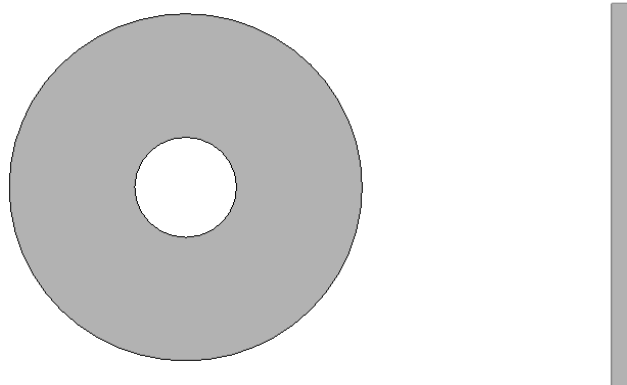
Vista en planta y perfil del pie de la válvula de impulso
